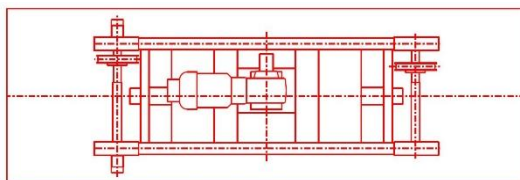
Zobrazenie priečného pásového dopravníka na layoute [1].
